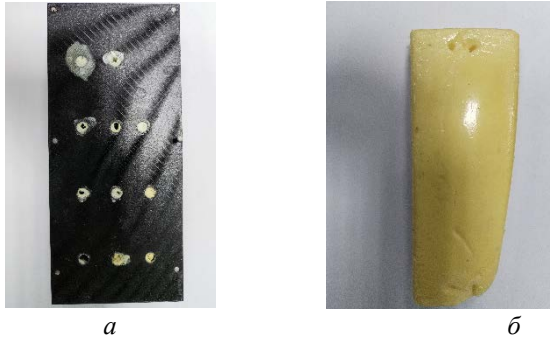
а – форма для виготовлення елемента БПЛА крило;
